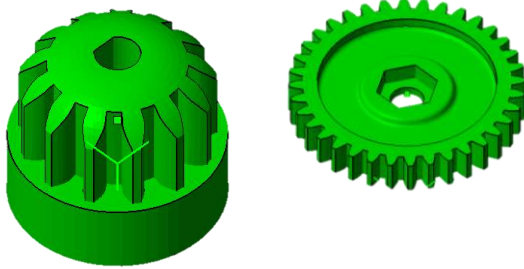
D'esquerra a dreta, engranatge petit i engranatge gran
